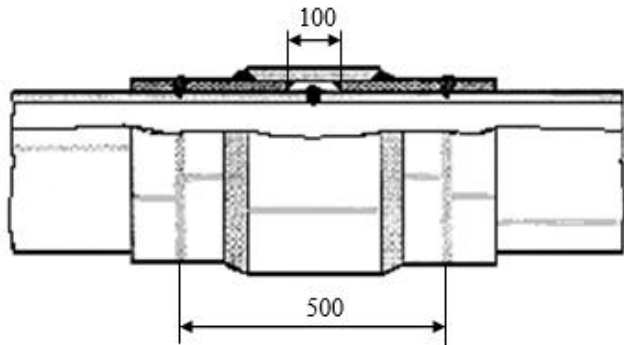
Муфта галтельная сварная типа П5 [3]
